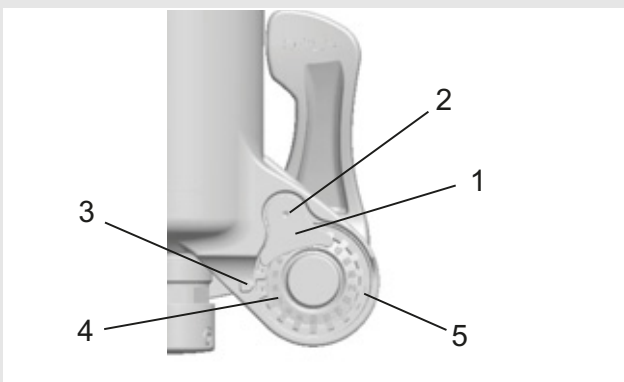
Vista posteriore della struttura del bloccaggio rapido con sicura del dado dell'asse (1) e dado dell'asse (5)
